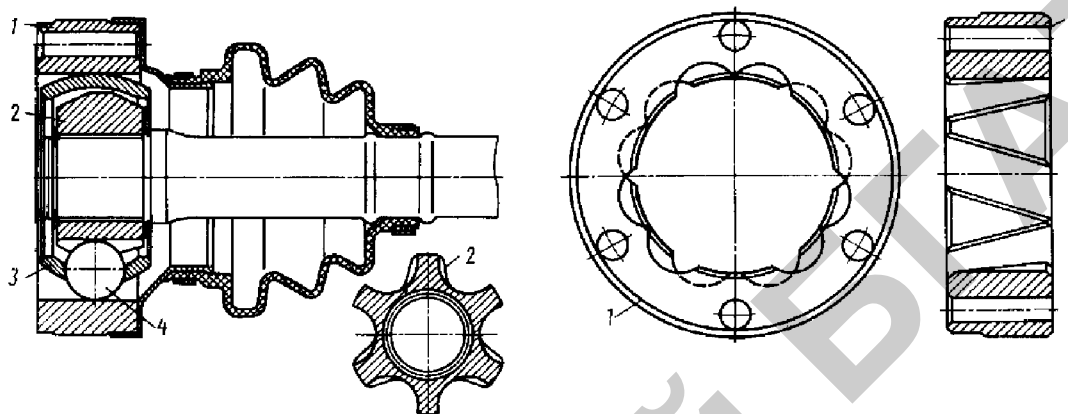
Шариковый универсальный карданный шарнир (типа «Леброс»)
